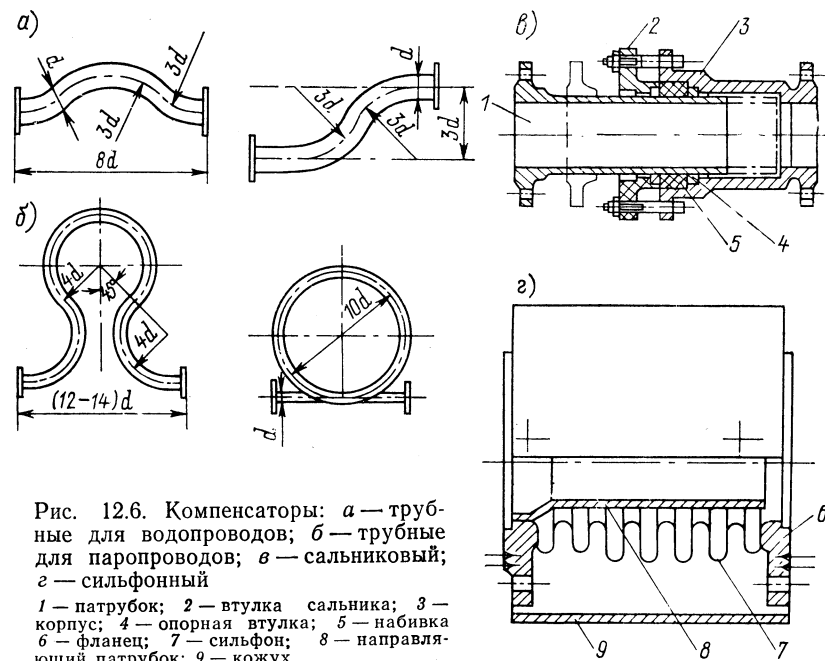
Компенсаторы: а — трубные для водопроводов; б — трубные для паропроводов; в — сальниковый; 1 — патрубок; 2 — втулка сальника; 3 — корпус; 4 — опорная втулка; 5 — набивка; 6 — фланец; 7 — сифон; 8 — направляющий патрубок; 9 — кожух
